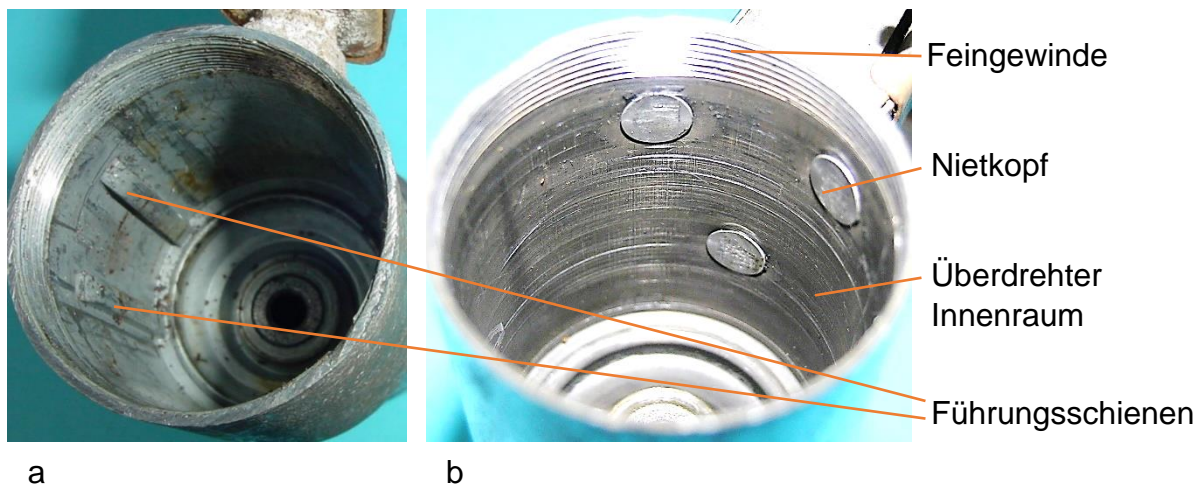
Gehäusetöpfe der Blätterpol-Dynamos: a) Eingegossener Drehbolzen, b) Angenieteter Flansch
